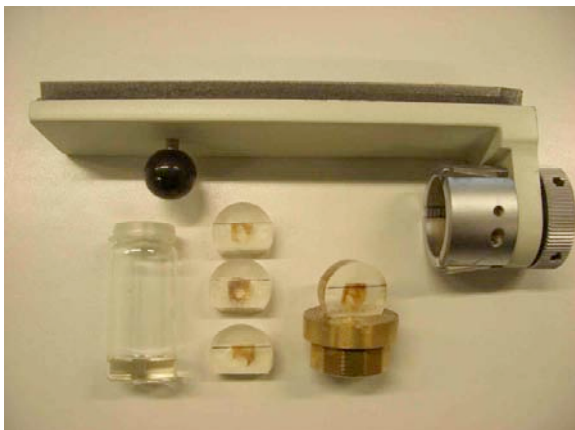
Einbettgläser, zugeschnittene Zylinder, aufgeklebte Probe und Halterung der Innenlochsäge
